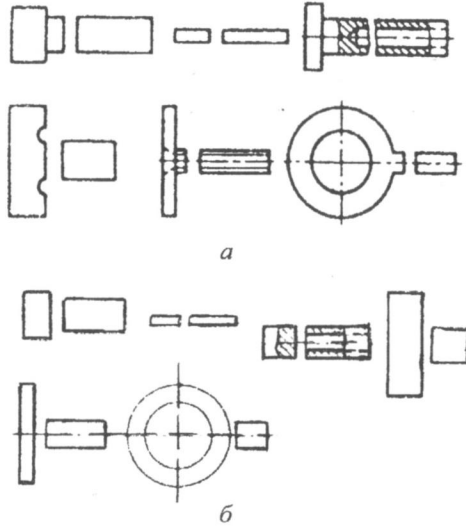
Типы сварных соединений, выполняемых стыковой сваркой: *а* – сопротивлением; *б* – оплавлением
